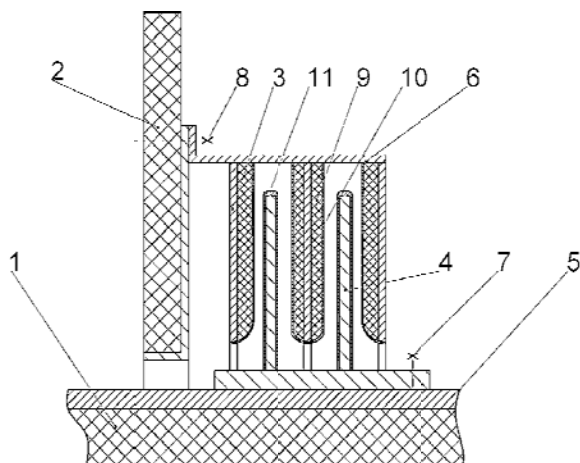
Лабиринтное уплотнение барабанной сушилки [4]: 1 – барабан; 2 – камера; 3 – неподвижные кольца; 4 – подвижные кольца; 5 – кольцевая опора; 6 – манжеты; 7 – шпилька; 8 – шайба; 9 – кольца из эластичного материала; 10, 11 – пленка из антифрикционного материала (фторопласт)
